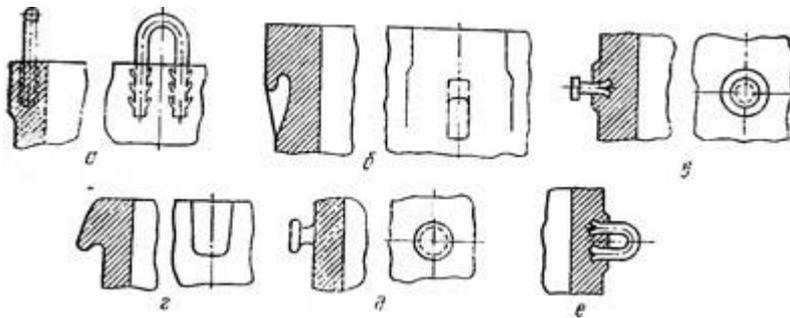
Конструктивные элементы для захвата изложниц при транспортировке: а — дужка; б — прилив с углублением; в — стальная цапфа; г — ухо; д — литая цапфа; е — скоба
